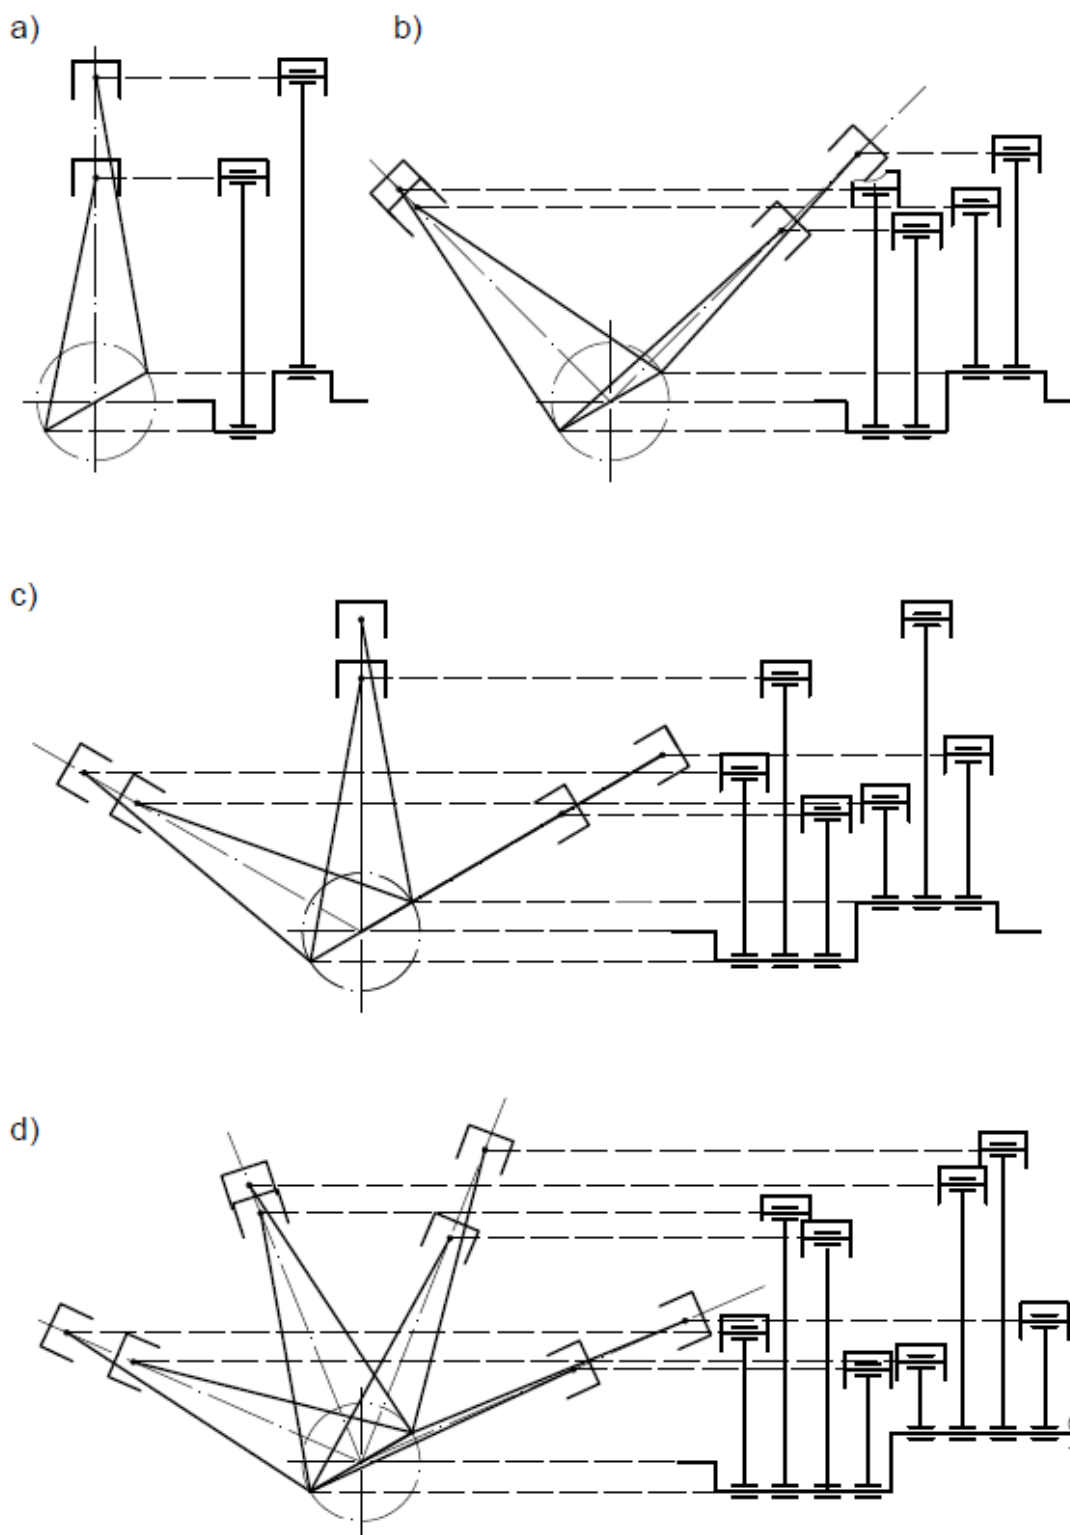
Кинематические схемы поршневых компрессоров с двухколенчатым валом:
